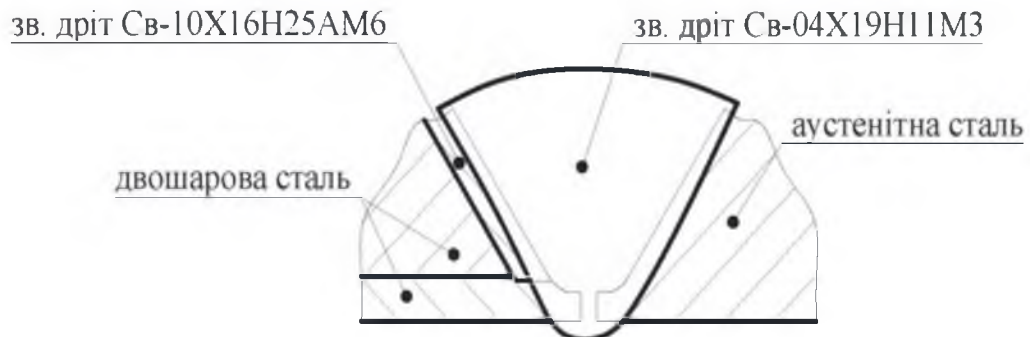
Зварне з'єднання двошарової сталі з деталлю із сталей аустенітного класу
